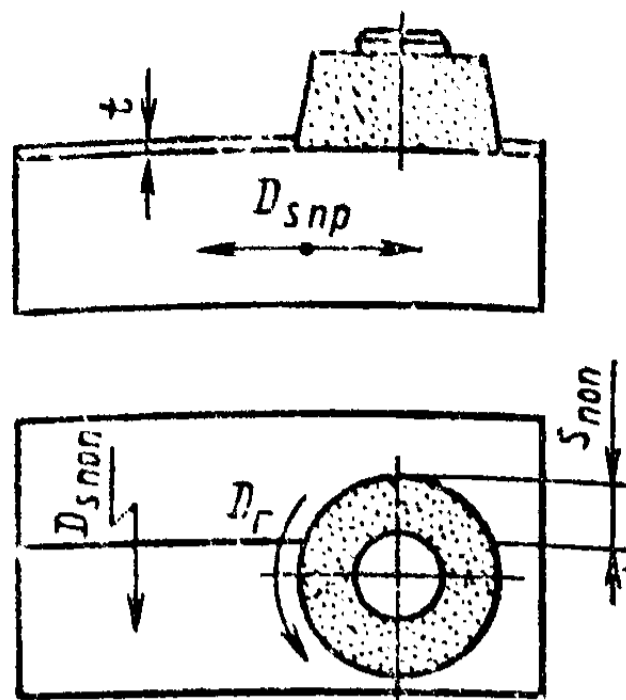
Схема обработки на плоскошлифовальном станке торцом чашечного круга
